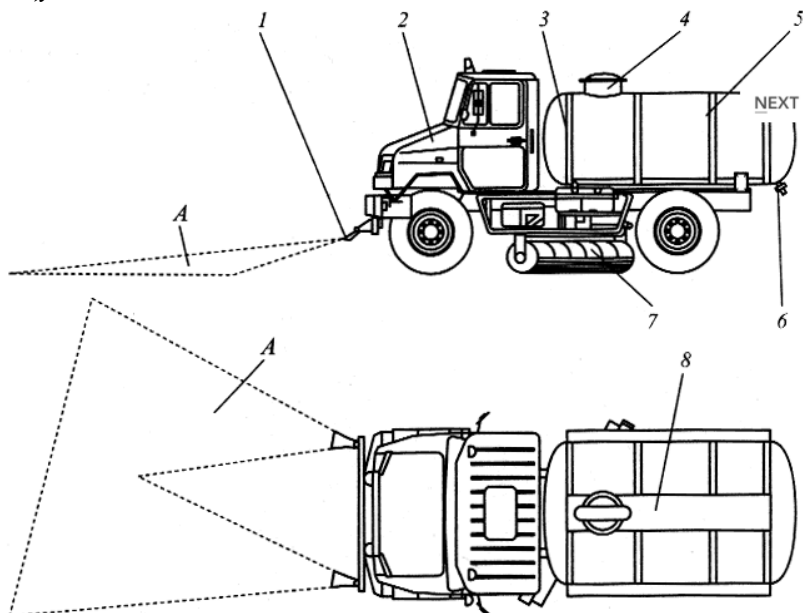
Компоновка и основные агрегаты поливо-моечной машины:
